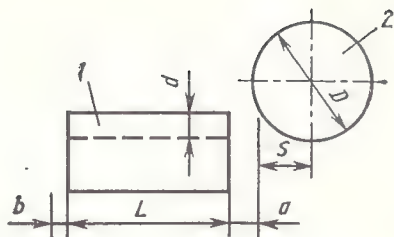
Расположение фрезы и детали (образующая детали находится ниже оси фрезы):
